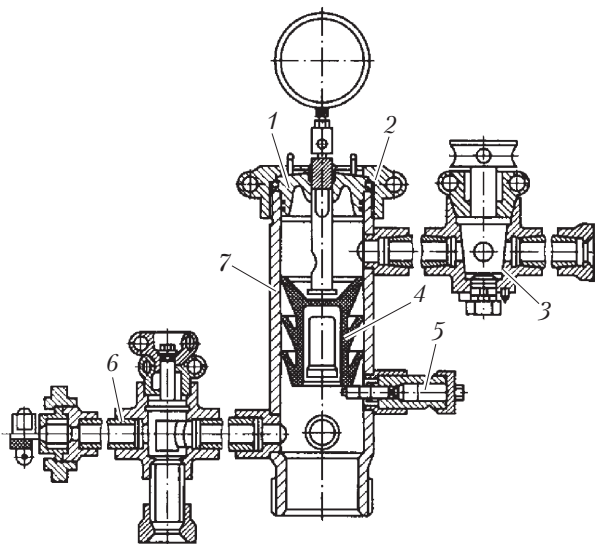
Конструкция головки цементировочной устьевой типа ГЦУ
